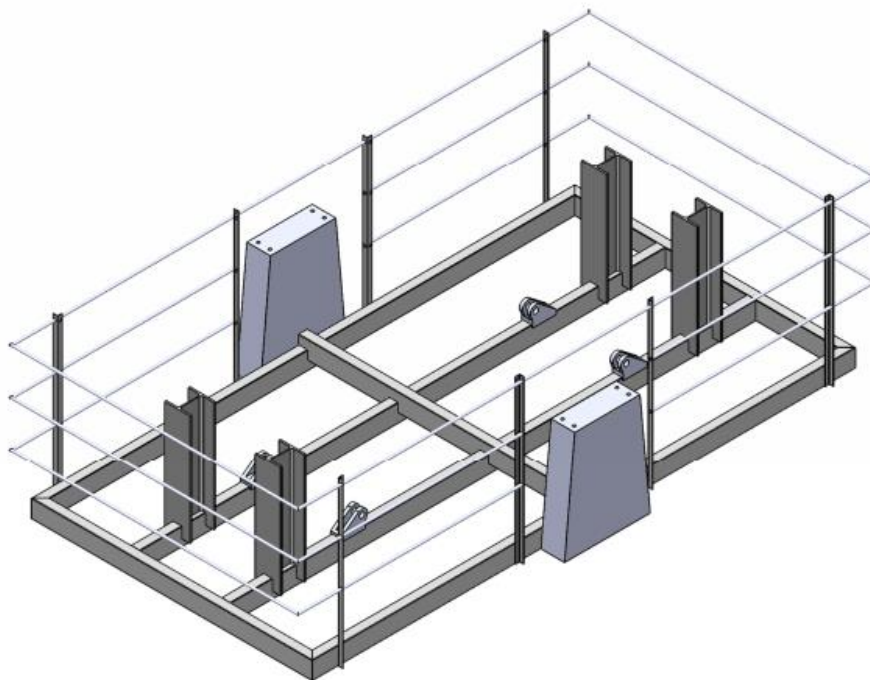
Subconjunto base: ligação de todos os componentes através do processo de soldadura.
